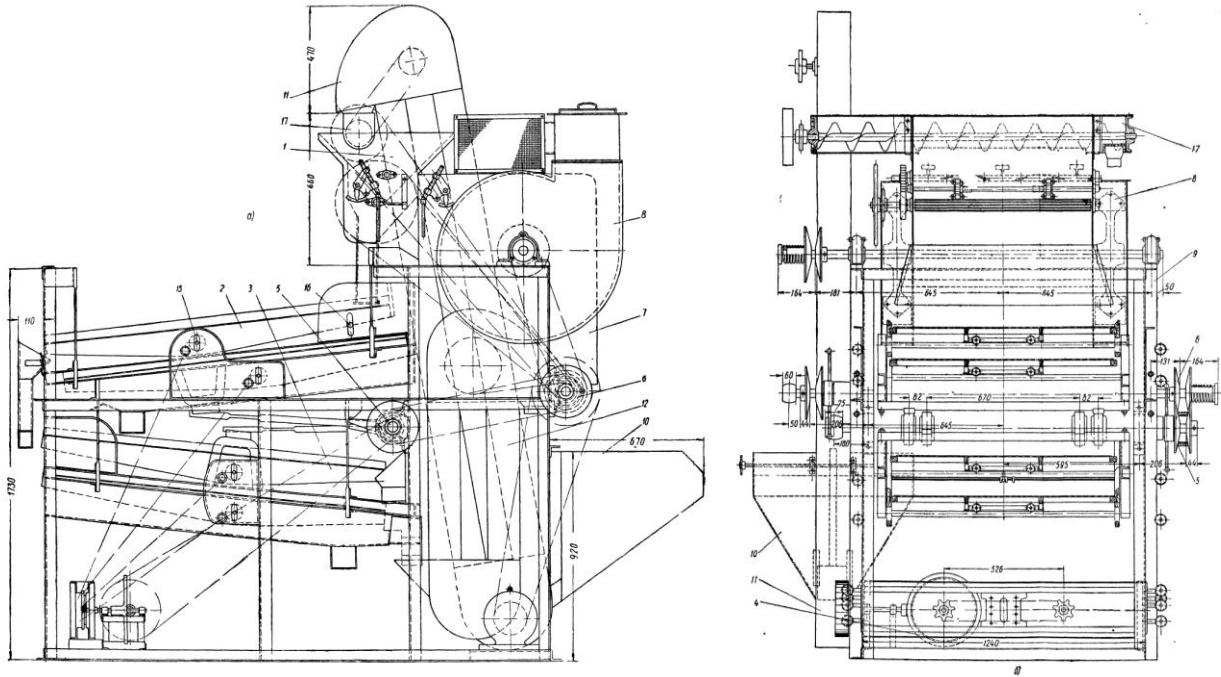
Загальний вигляд ОВР-4: 1 – засипний ківш; 2 – верхній решітний стан; 3 – нижній решітний стан; 4 – щітковий привід; 6 – ексцентриковий привід; 6 – головний привід; 7 – аспіраційна камера; 8 – вентилятор; 9 – рама, 10 – бункер, 11, 12 – елеватори I та II; 13 – передача до щіток; 14 – клинопасова передача; 16 – механізм підйому щіток; 16 – регулятор нахилу решіт, 17 – шнек
